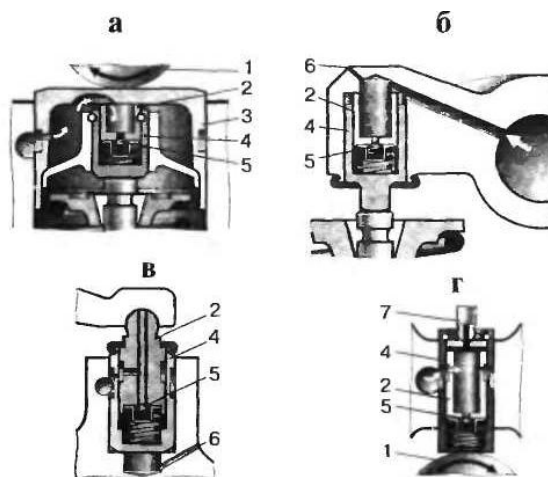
Гідравлічні штовхачі клапанного приводу: а - циліндричними штовхальниками; б - коромислами; в - важелями; г - двигунів
